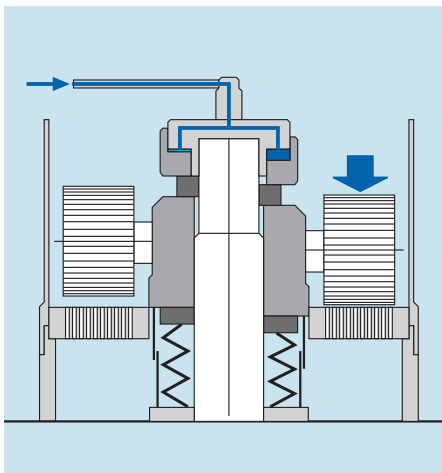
Funcionamiento del ajuste hidráulico del cabezal de rodillos: a la izquierda en posición libre, a la derecha en posición de trabajo
